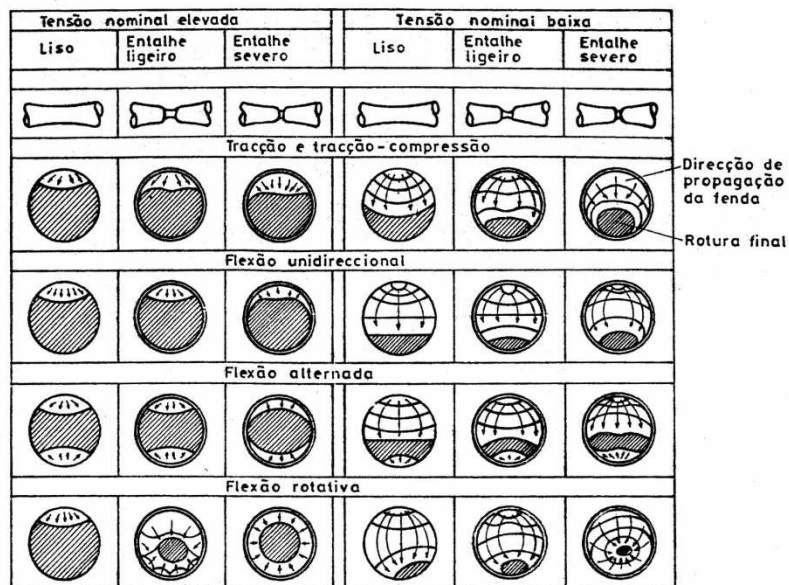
Aspecto característico de superfícies de fractura por fadiga [19].
